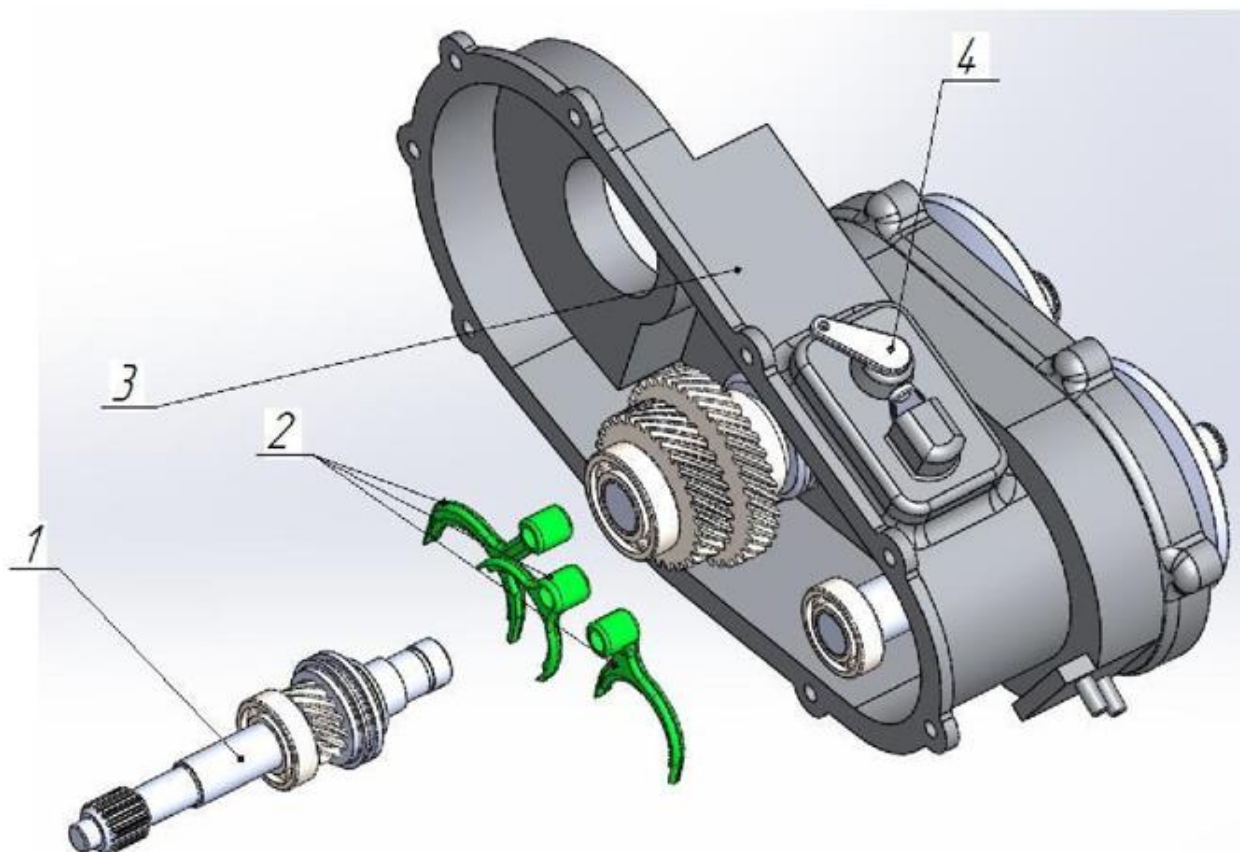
Механизм включения задней передачи: 1 – первичный вал; 2 – вилки включения задней передачи; 3 – корпус вариатора; 4 – механизм переключения
